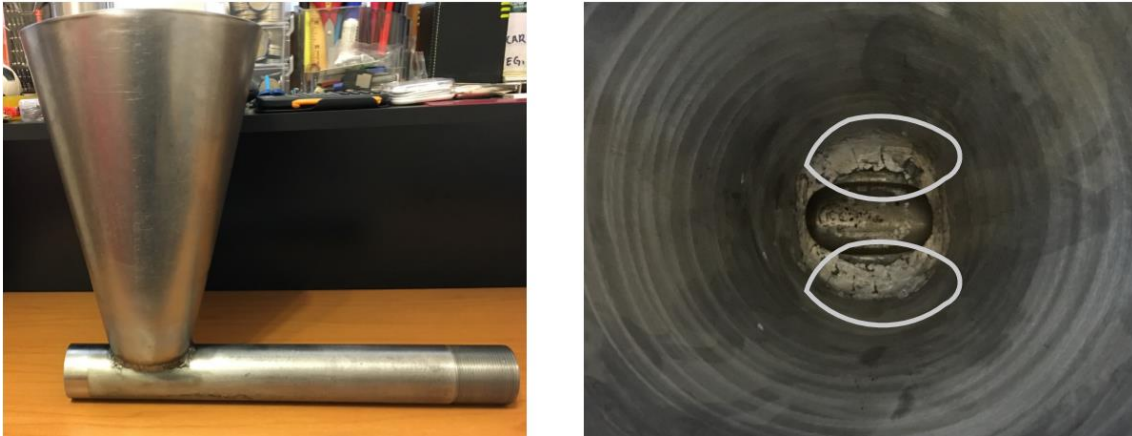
12 (a) Tolva soldada al cañón, (b) Problemas de alimentación de la tolva al cañón
